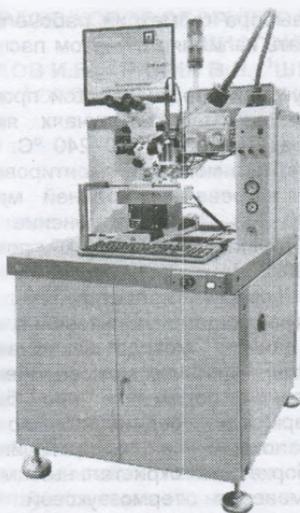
Установка термозвуковой сварки ЭМ-4450
